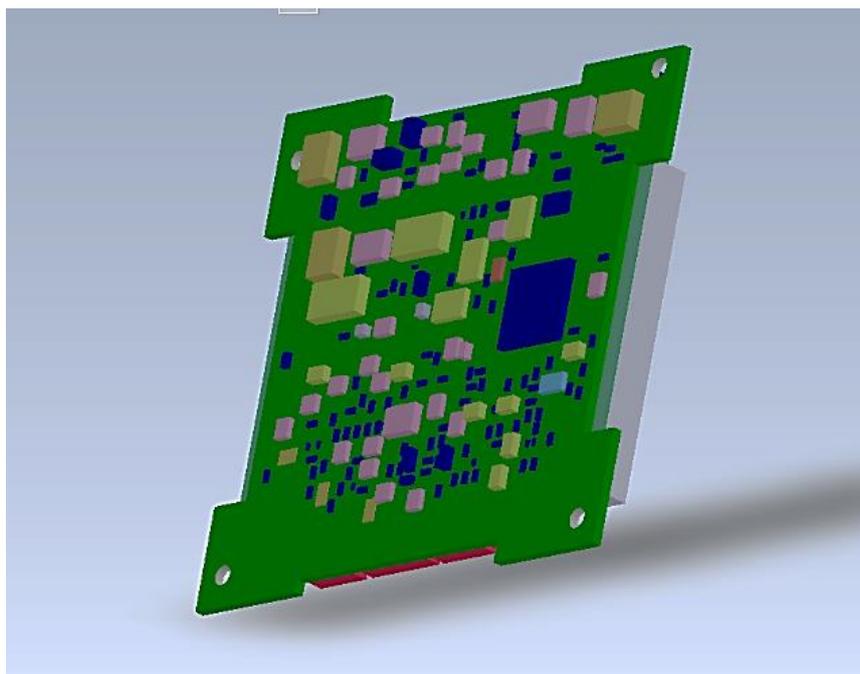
Rappresentazione 3D lato bottom del PCB con i componenti
